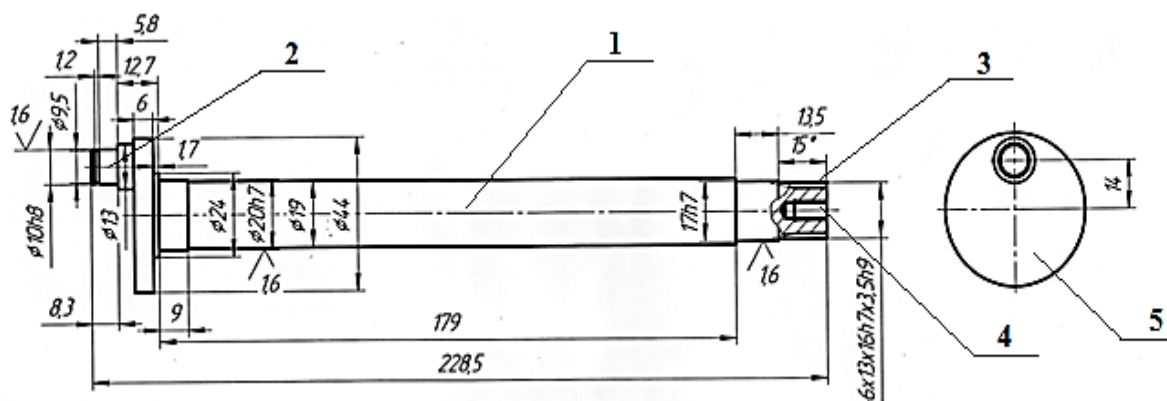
Конструкция кривошипного вала поворотного механизма
